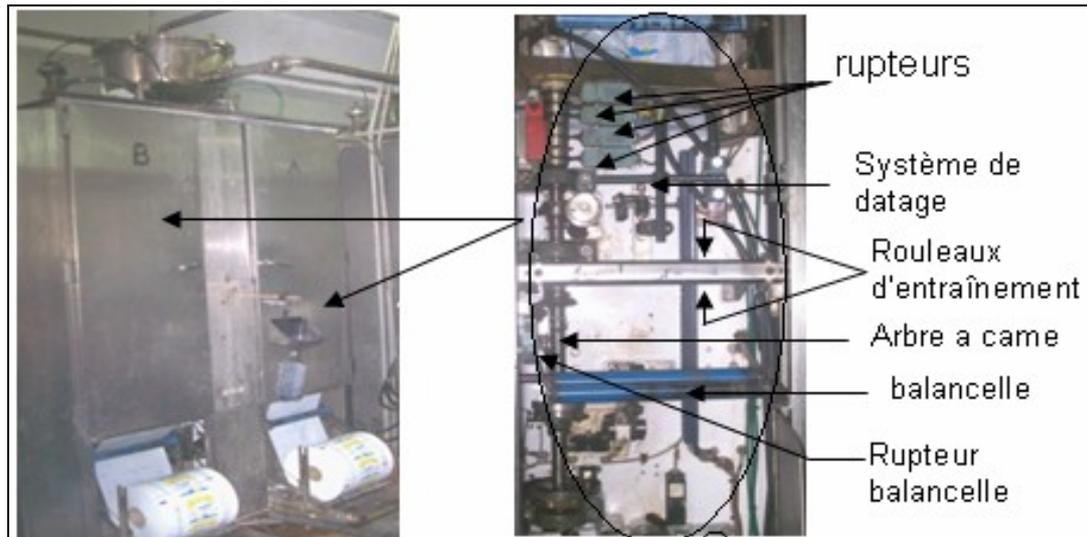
Emplacement de l'arbre à cames dans la machine.
